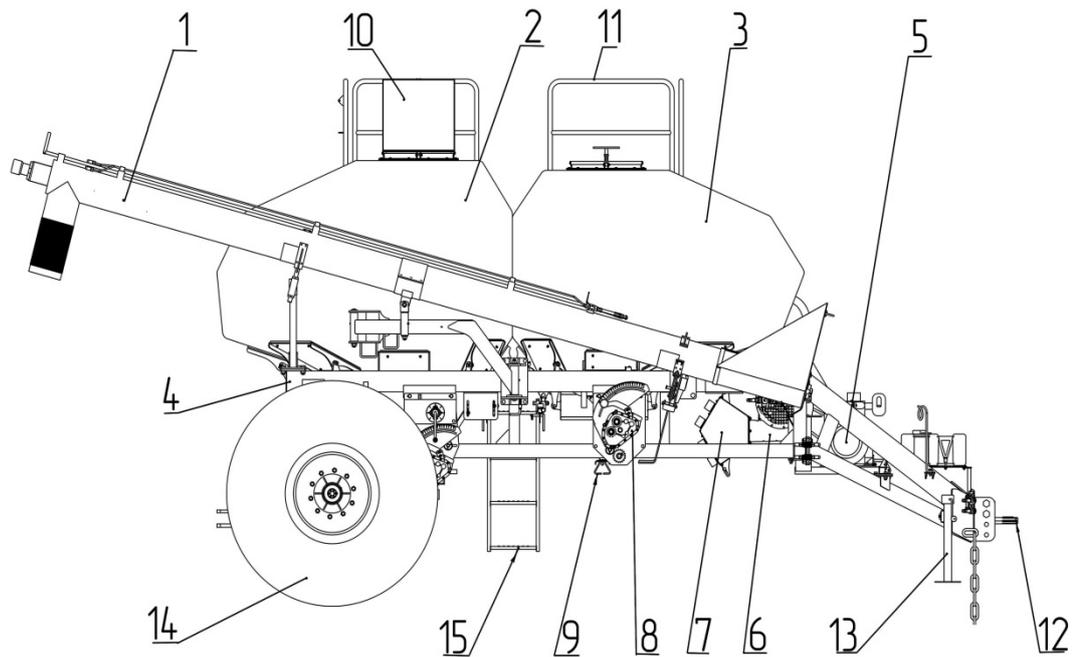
Посівна частина сівалки-культиватора пневматичної широкозахватної «ALCOR 7,5»:
